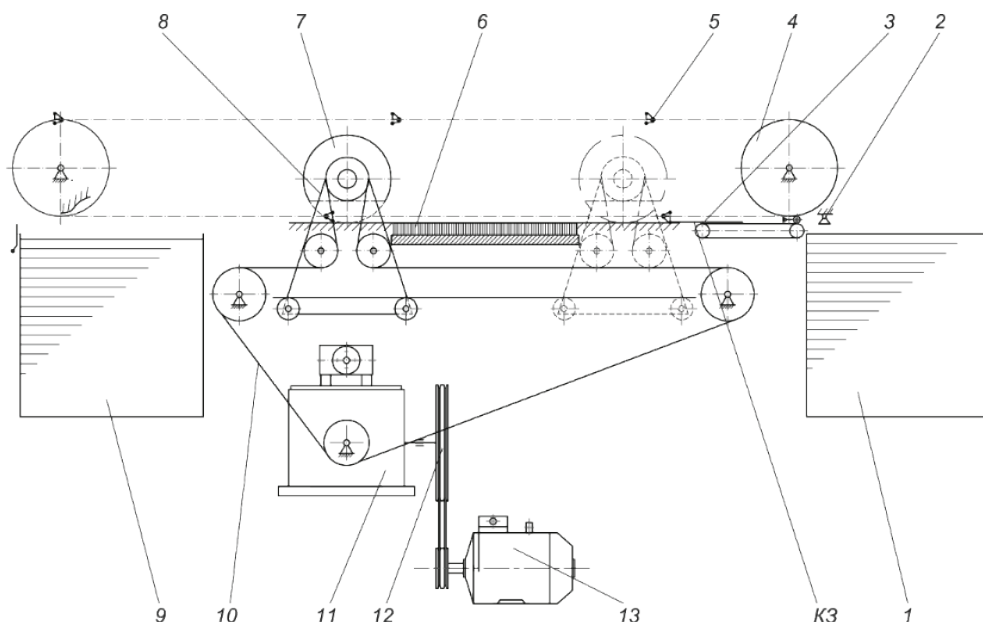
Кінематична схема плоскоциліндрового штанцювального преса:
